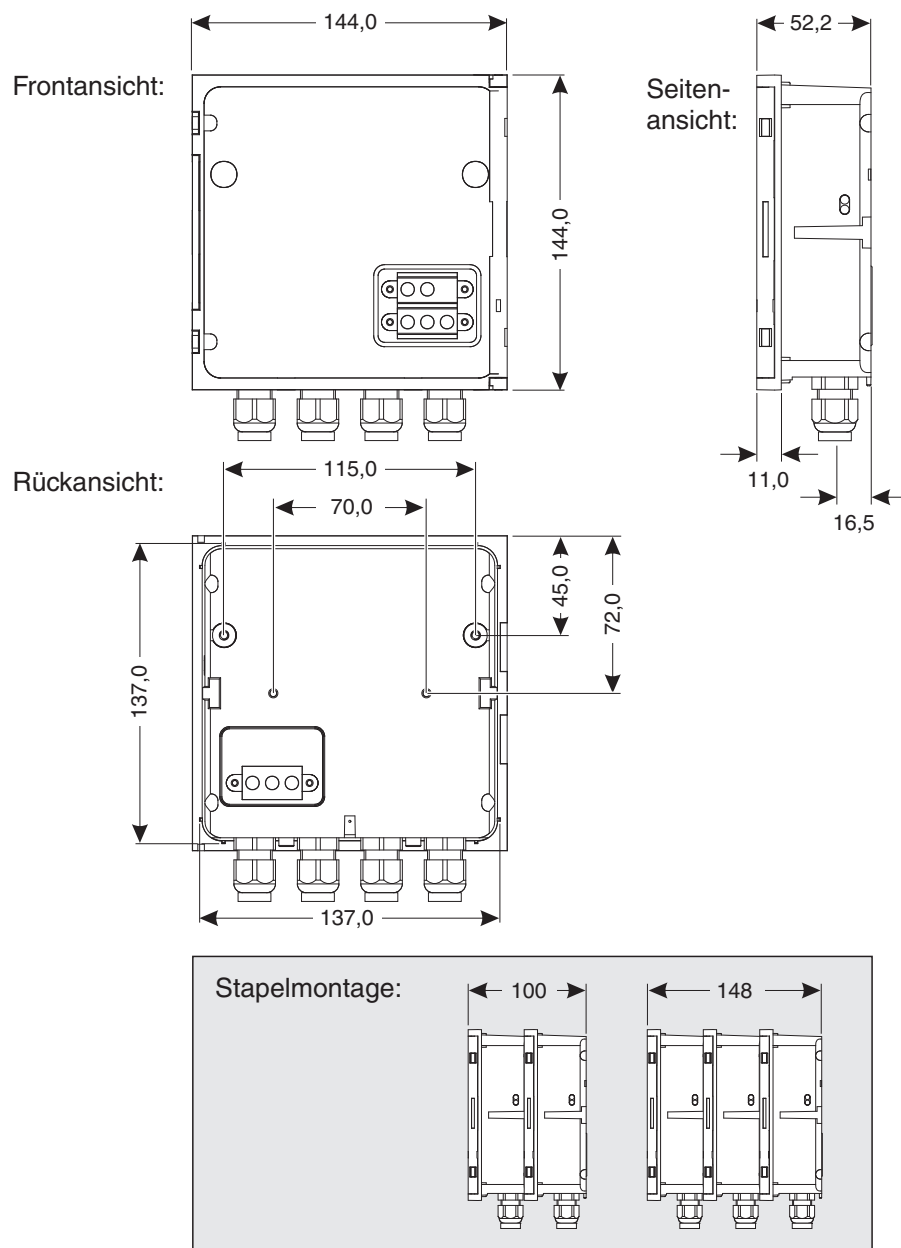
Maßzeichnung MIQ Modul (Maße in mm)
